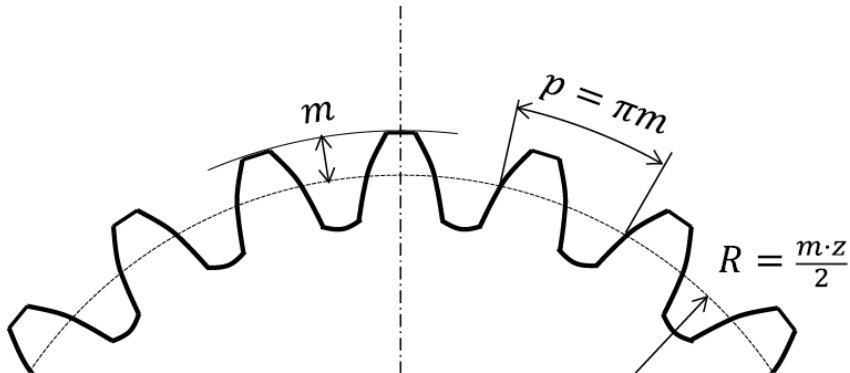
Dimensiones principales del engranaje respecto al módulo[11]
